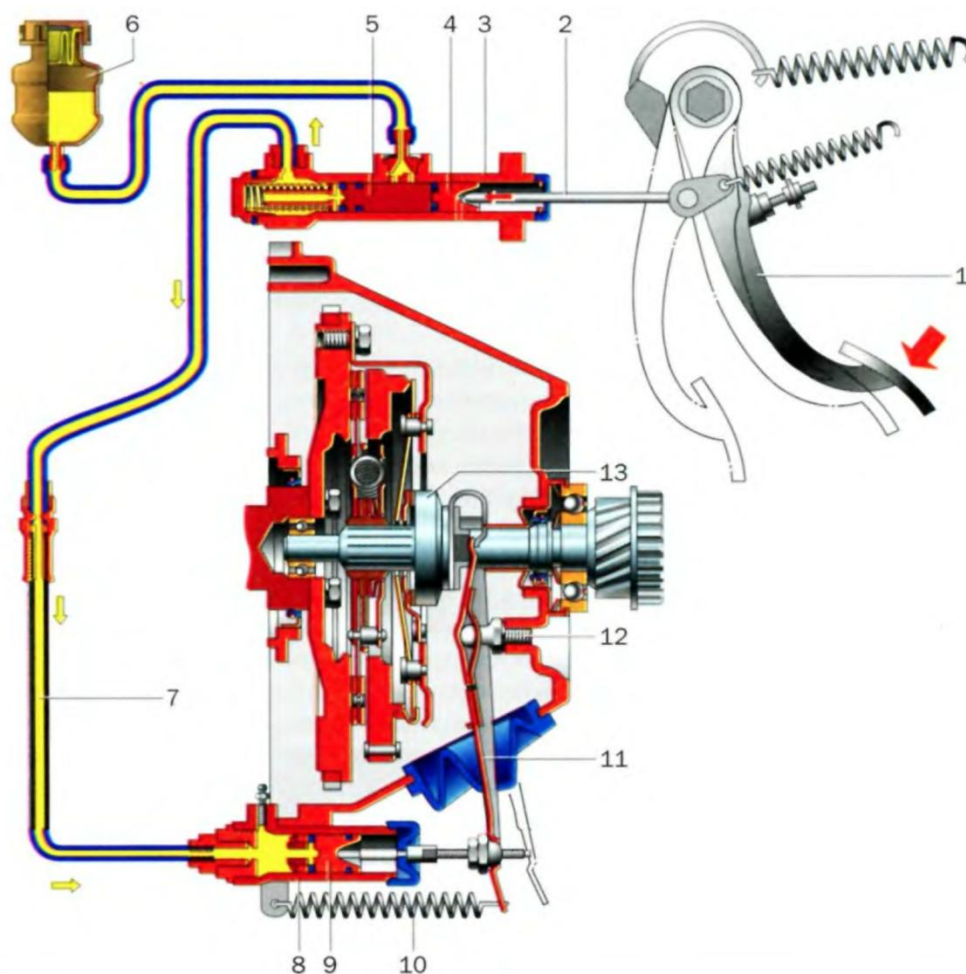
Схема гидравлического привода сцепления: 1 — педаль; 2 — толкатель; 3 — главный цилиндр; 4 — поршень толкателя; 5 — поршень главного цилиндра; 6 — бачок; 7 — трубопровод; 8 — рабочий цилиндр; 9 — поршень; 10 — пружина; 11 — вилка; 12 — опора вилки; 13 — выжимной подшипник
